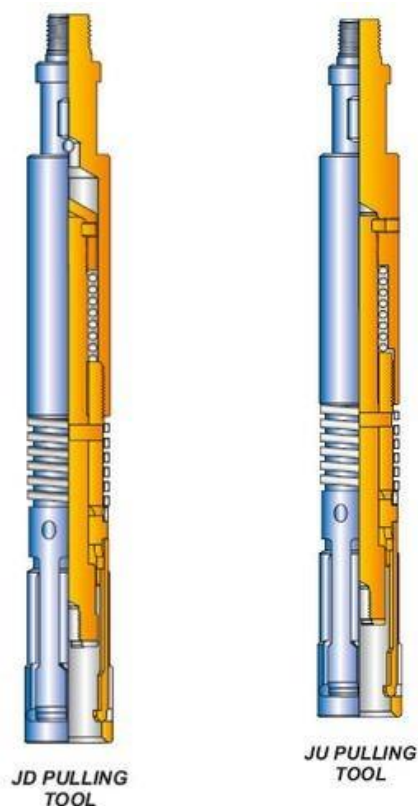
Инструмент подъемный ‘JD’ и ‘JU’
